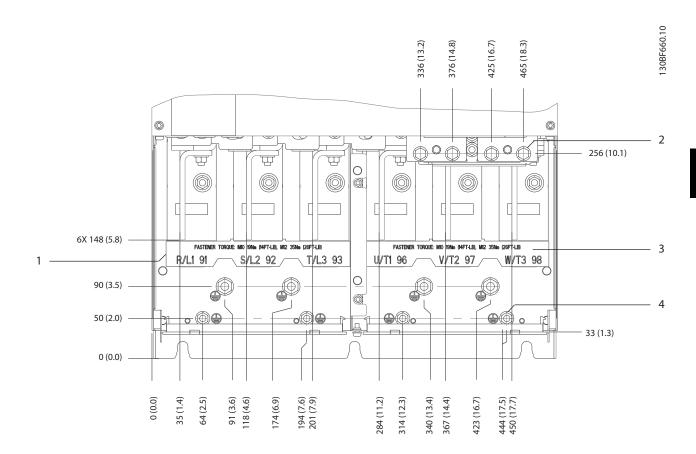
Dimensions des bornes E2h (vues latérales)
